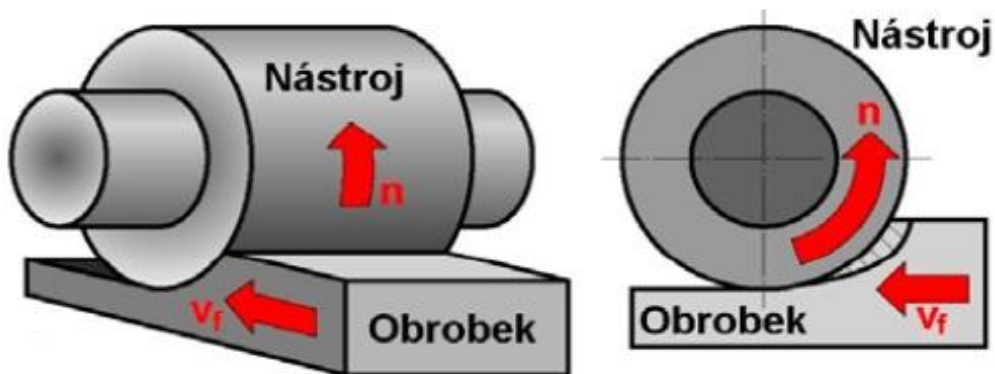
Frézování válcové (obvodové) a čelní [8]
